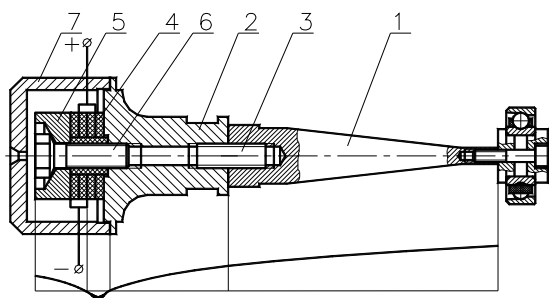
Приспособление для пластического деформирования нитиноловой проволоки
